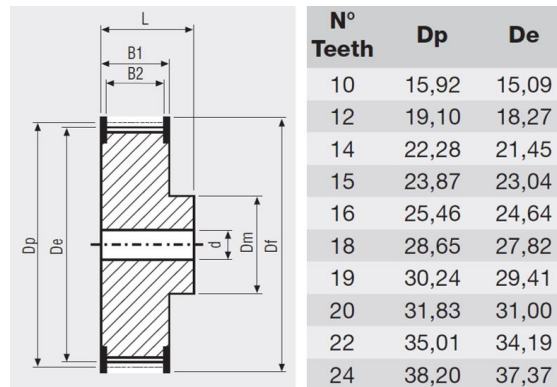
Polea motriz: Z , D_p y De . Fuente: Megalinear pág. 28 [22].
